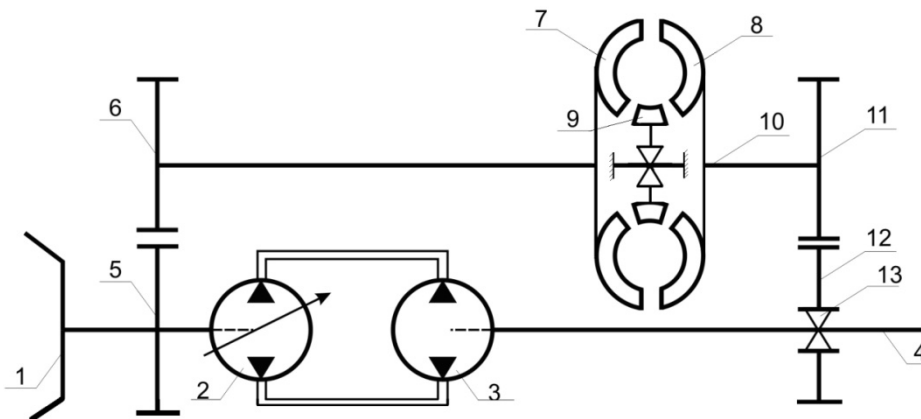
Кинематическая схема бесступенчатой коробки передач
